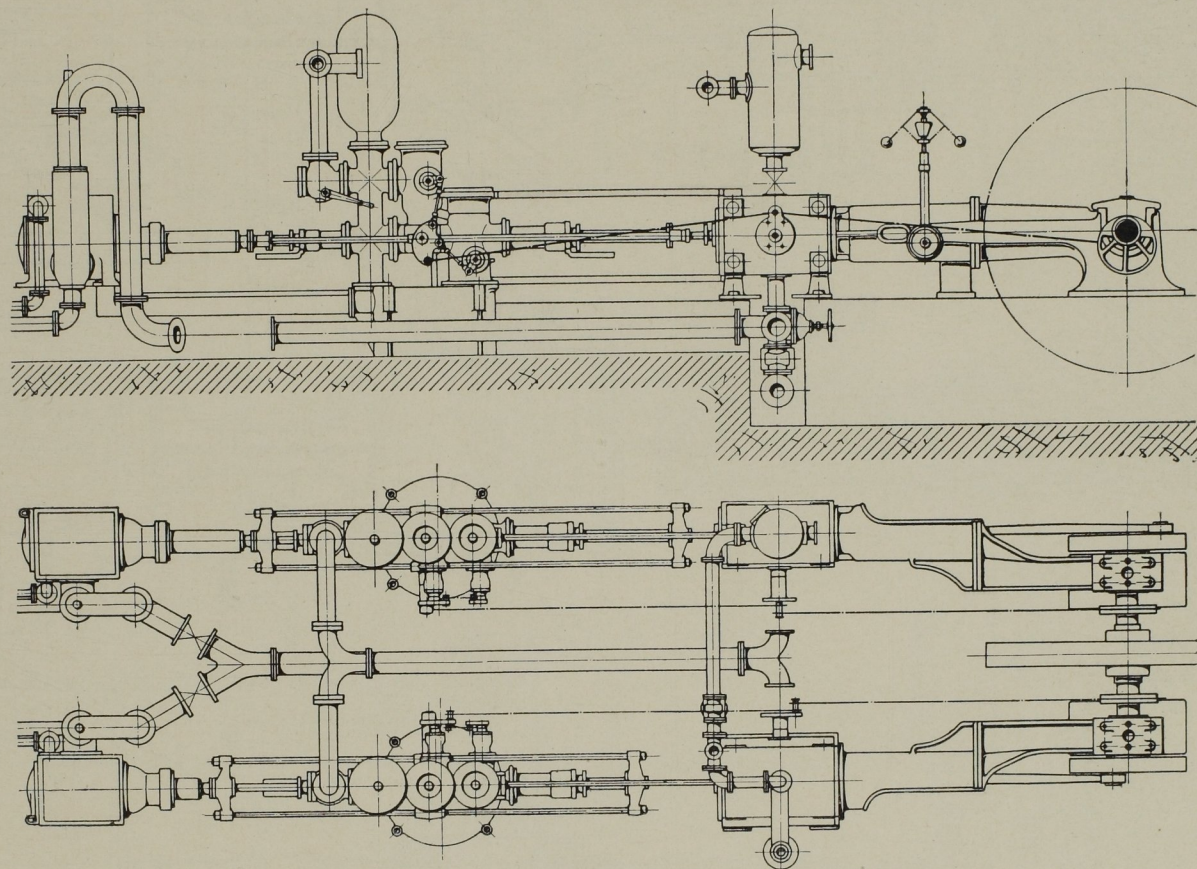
Seitenansicht und Grundriss. Masst. 1:72.
